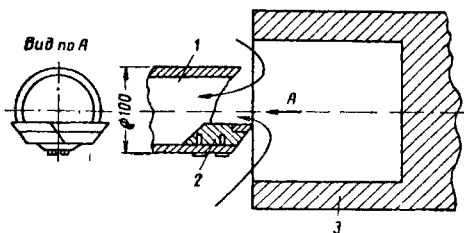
Местный отсос для обдирки, торцовки и внутренней расточки изделий
